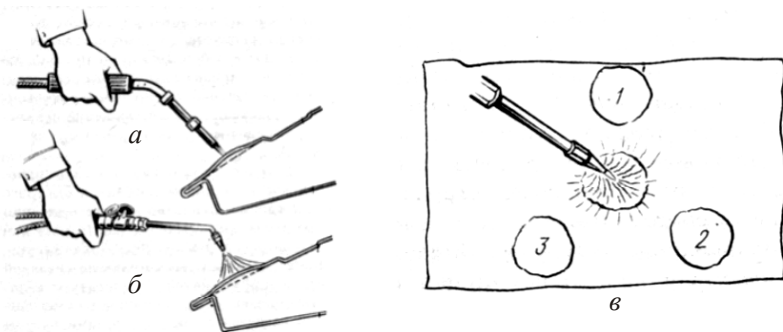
Устранение выпуклостей на поверхности кузова методом нагрева и быстрого охлаждения: *а* – нагрев металла угольным электродом сварочного аппарата; *б* – нагрев металла пламенем газовой горелки; *в* – последовательность охлаждения нагретой поверхности кузова с выпуклостью
